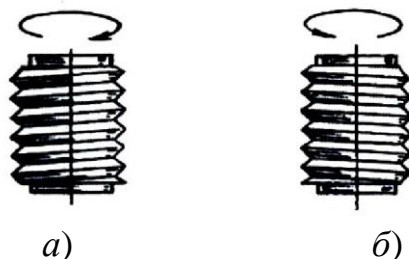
Виды резьбы по направлению витков: *а* – правая резьба; *б* – левая резьба
